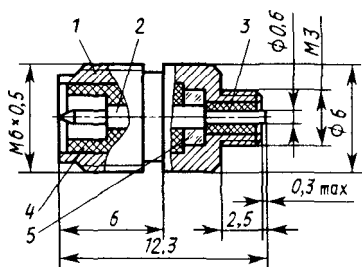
Конструкция герметичного коаксиального соединителя: 1—корпус; 2—штырь; 3, 4—изоляционные втулки из фторопласта; 5—стеклянная таблетка
